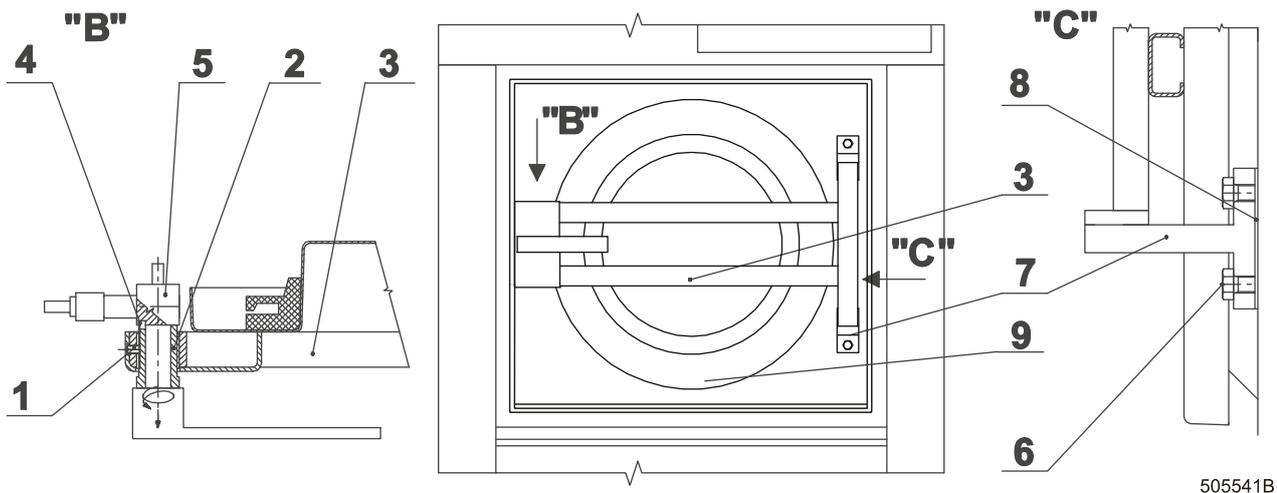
A Máquinas 33-40-55 kg / 75-90-125 lbs
